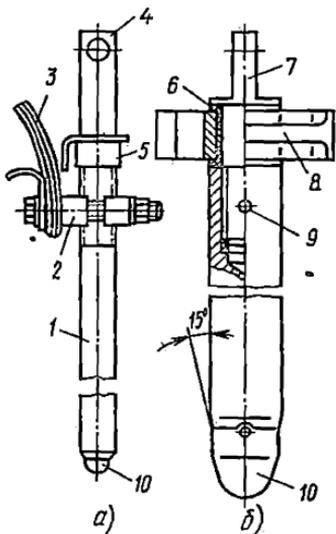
Подвижный контакт: а — выключателя ВМГ-10, б — то же, ВМП-10; 1 — стержень, 2 — контактная колодка, 3 — гибкая связь, 4 — наконечник с проушинами, 5 — контргайка, 6 — втулка, 7 — головка, 8 — направляющая колодка, 9 — штифт, 10 — наконечник
